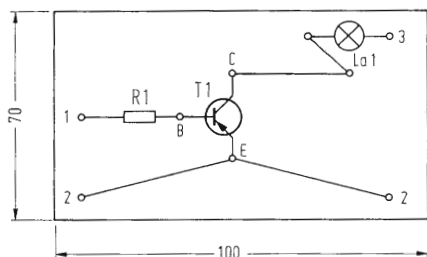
Schema di montaggio su tavoletta dell'interruttore per lampada ad incandescenza
